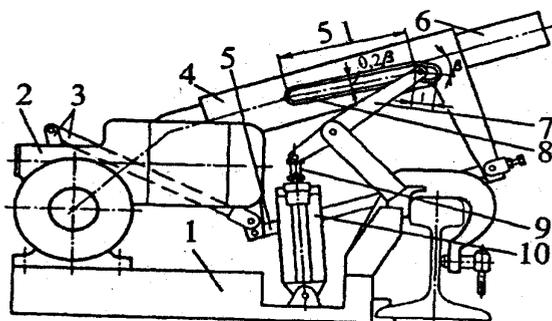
Устройство рельсорезного станка РМ-5Г
